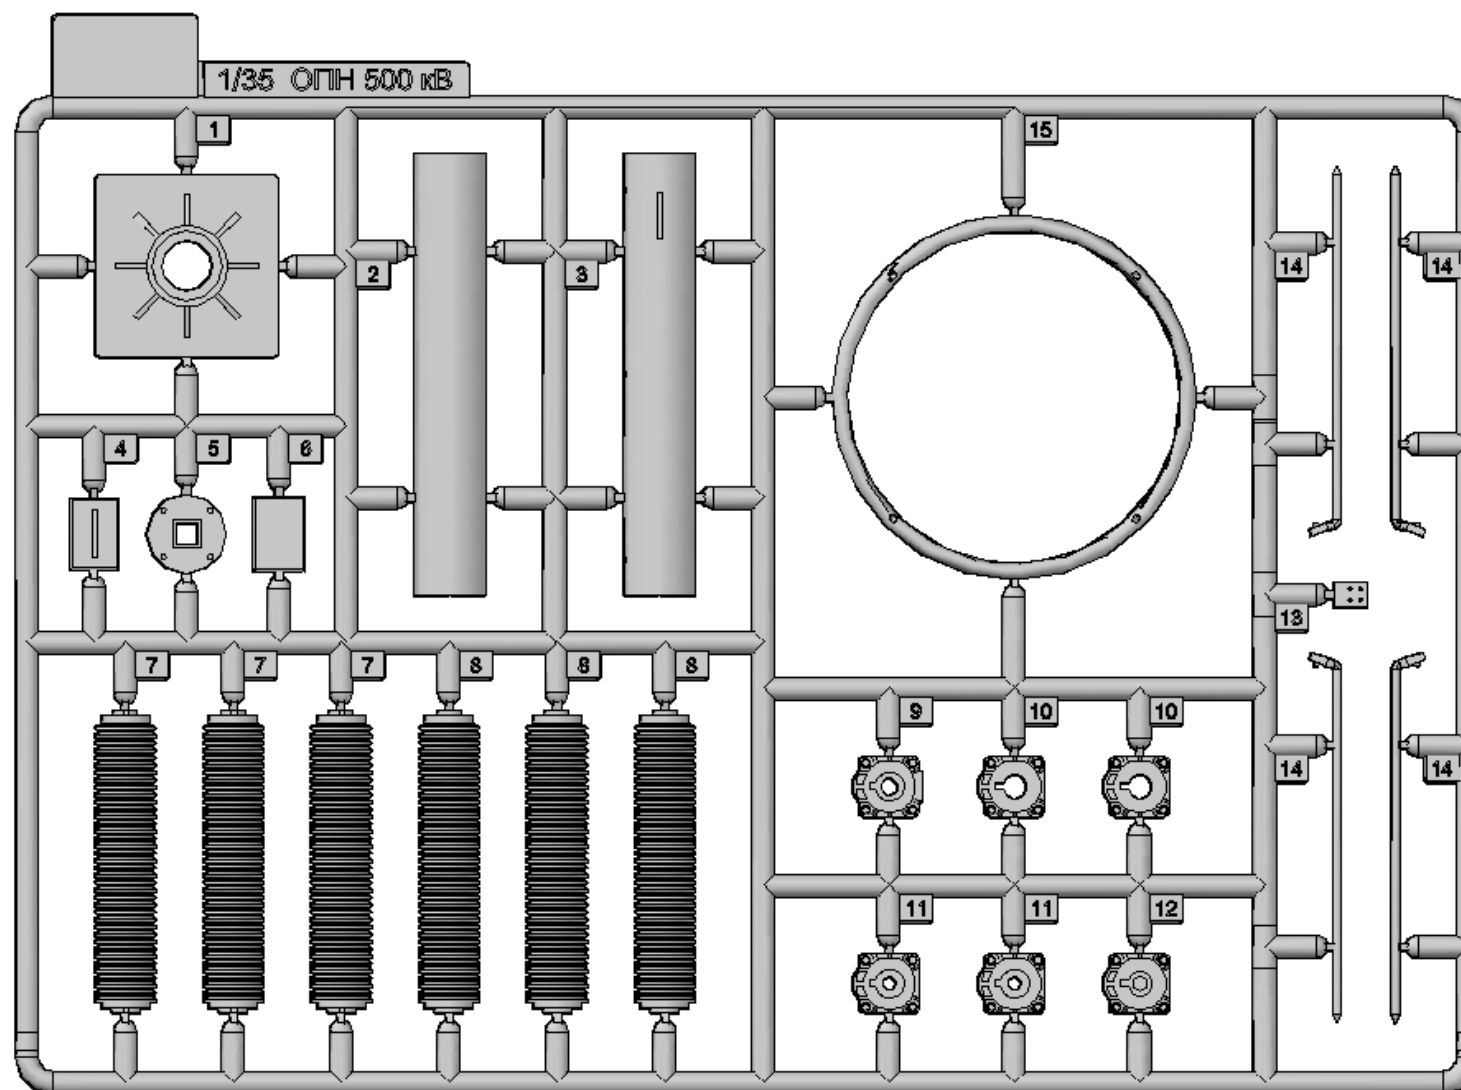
Внешний вид оптимизированного технологического конструктора ограничителя перенапряжений 500 кВ, вид сверху. Промышленный серийный образец
